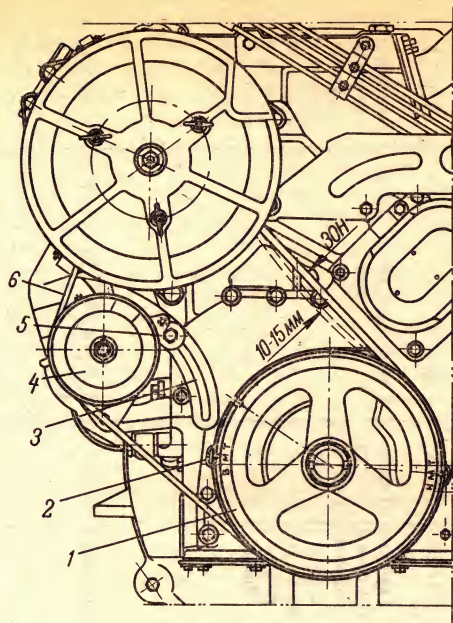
Устройство для натяжения ремня привода вентилятора и генератора двигателя Д-37Е:
